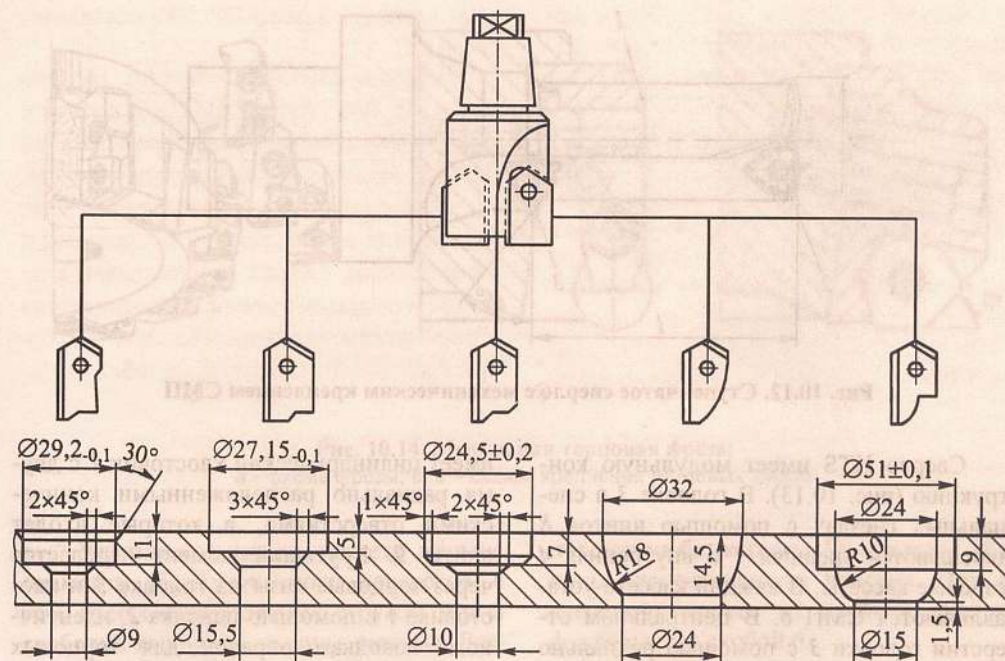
Примеры отверстий, обрабатываемых сборными зенкерами
